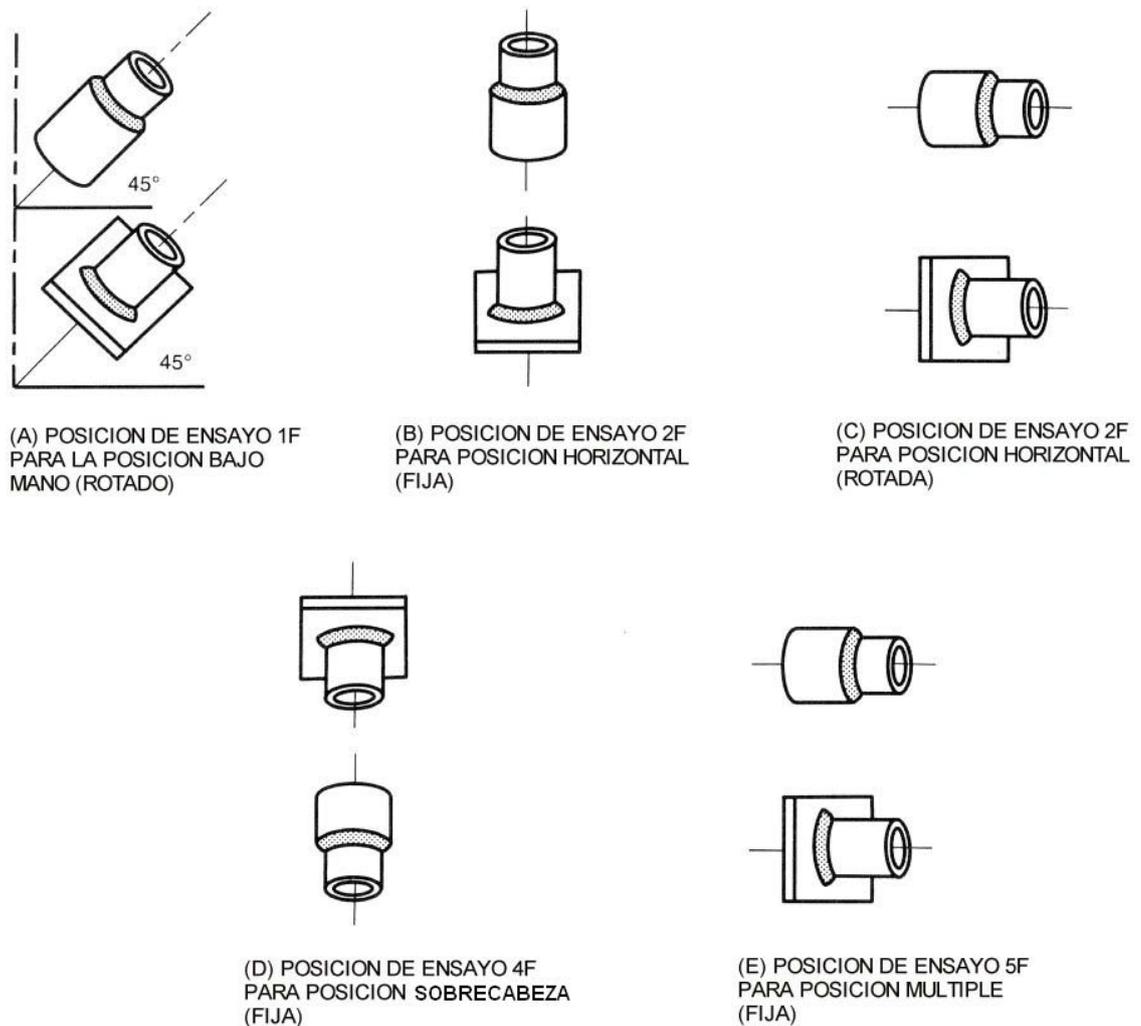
Posiciones para ensayo de tubos o caños para soldadura de filete
